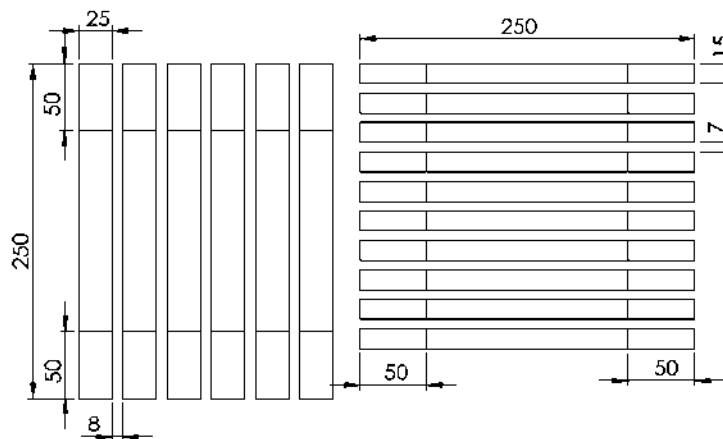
32 Plano del segundo corte con chorro de agua, para obtener las probetas
